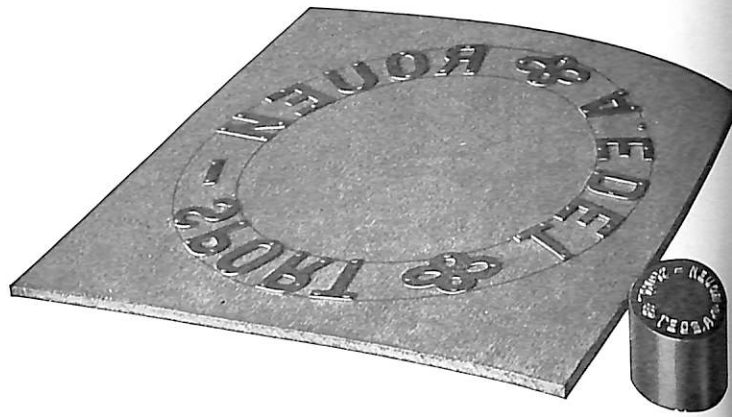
Skelettschablonen, mit Stiften auf Sperrholzplatte befestigt; daneben der gravierte Stempel
